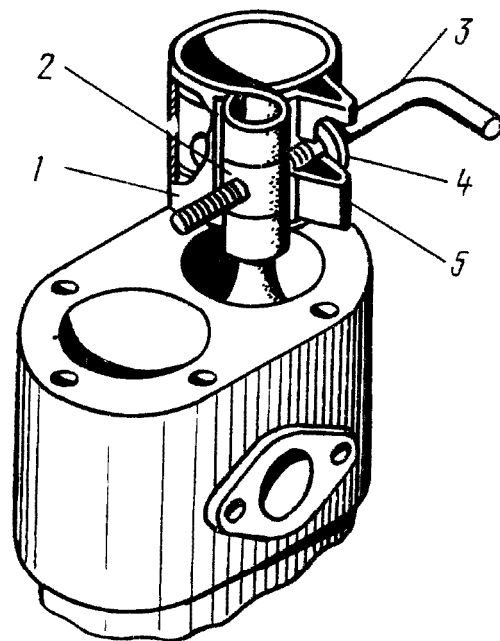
Установка поршня в сборе с шатуном и кольцами в цилиндр блока компрессора приспособление: 2494.
